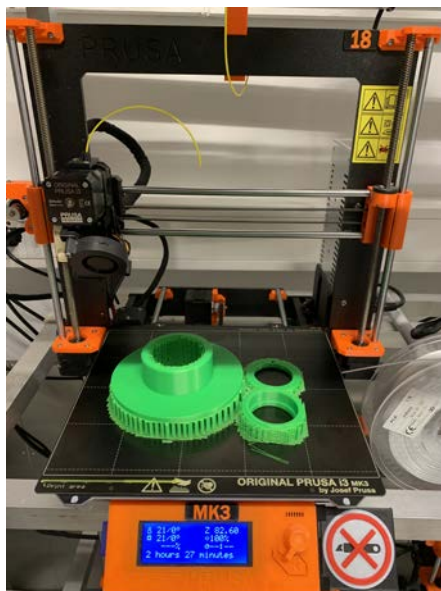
Надруковані деталі на 3d-принтері
